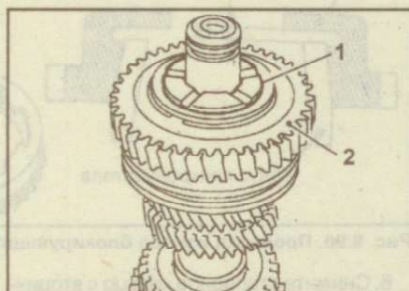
Снятие упорной шайбы (1) и шестерни (2) передачи заднего хода с вторичного вала
